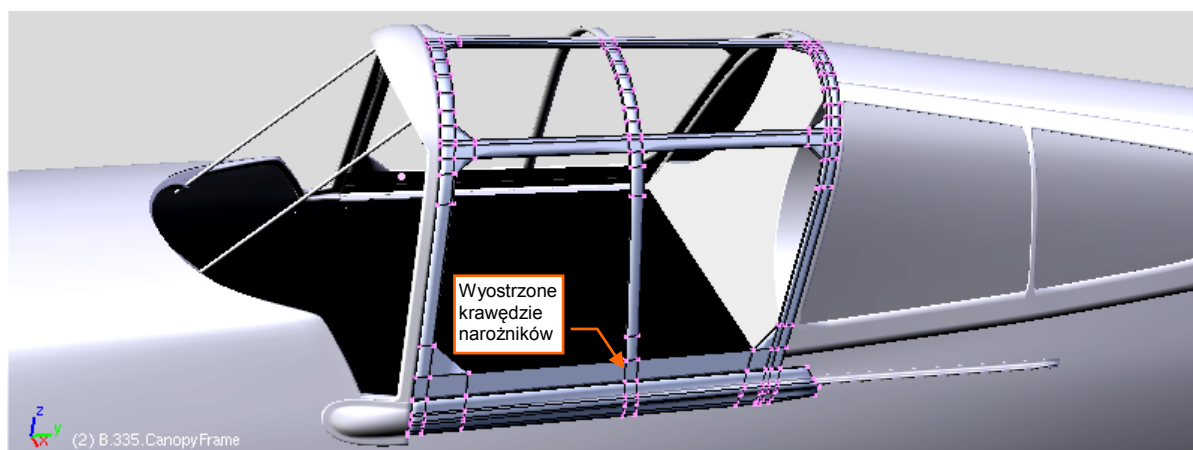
Przygotowanie zarysu wewnętrznych krawędzi ramki
